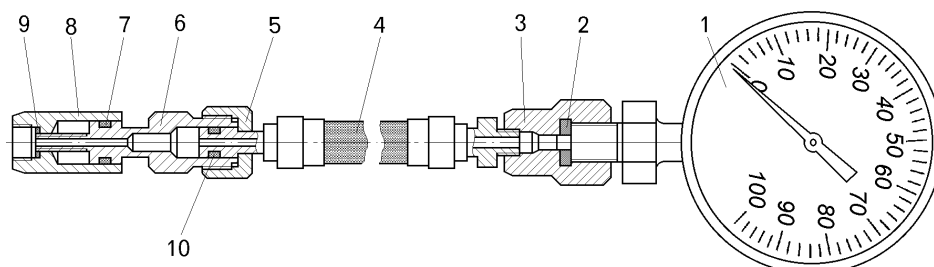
Приспособление для замера давления в цилиндрах:
